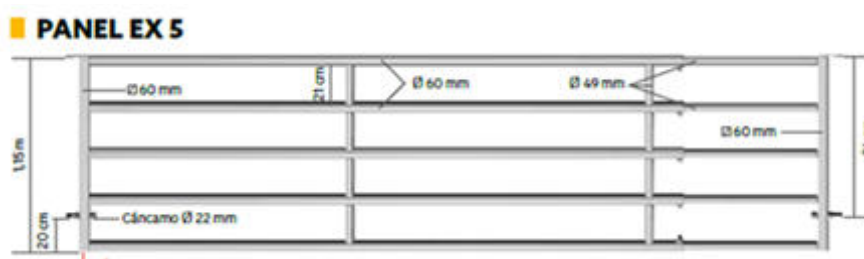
Perfil transversal portillos extensibles de 3-4 y 4-5 metros de anchura y 2" de espesor
